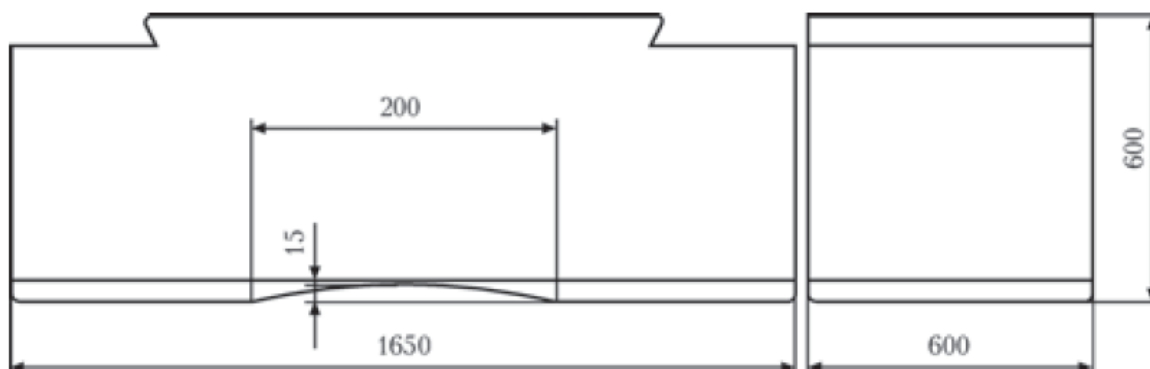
Выработка рабочей поверхности бойка прессы
